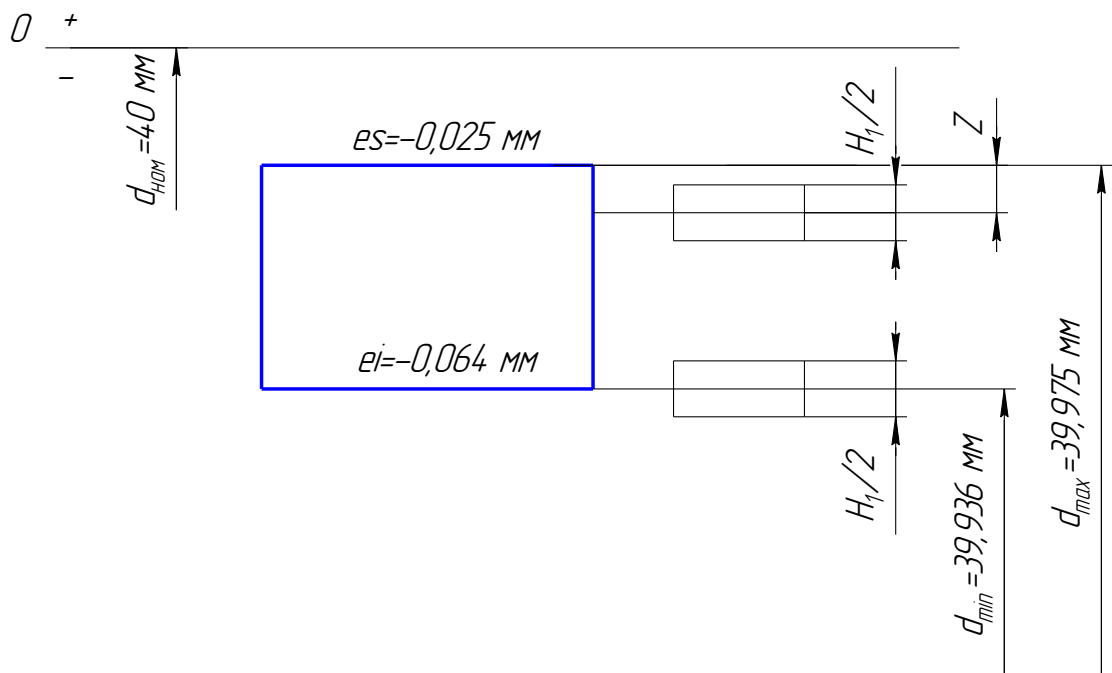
Схема розташування допусків робочих поверхонь скоби для контролю розміра $\varnothing 40f8 \begin{smallmatrix} -0,025 \\ -0,064 \end{smallmatrix}$
